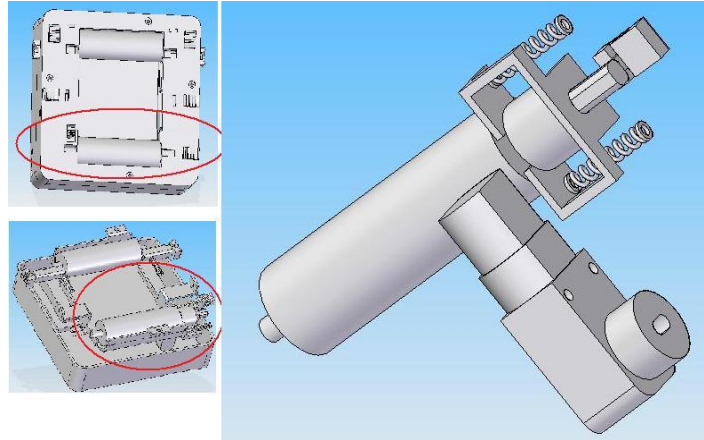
Vista inferior de las partes que componen la etapa de transmisión para el rodillo.
